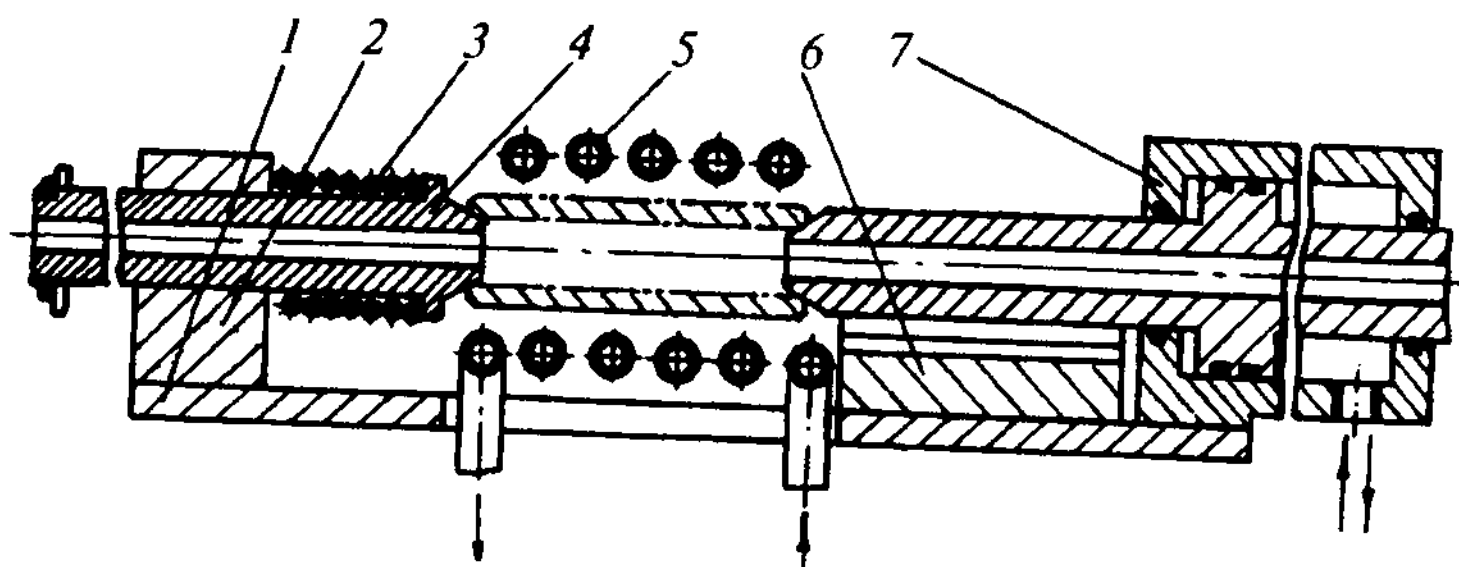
Схема станда для термопластической раздачи поршневых пальцев:
